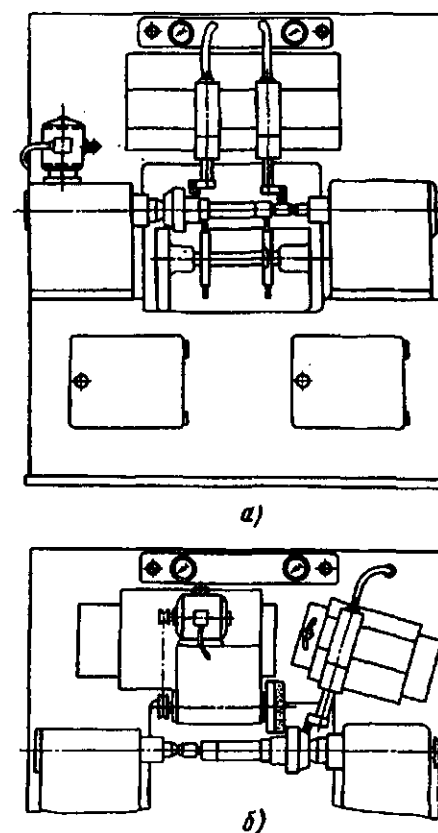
Схема суперфинишной обработки вала коробки передач на двухпозиционном автомате: а – цилиндрических шеек; б – конической и торцевой поверхностей
